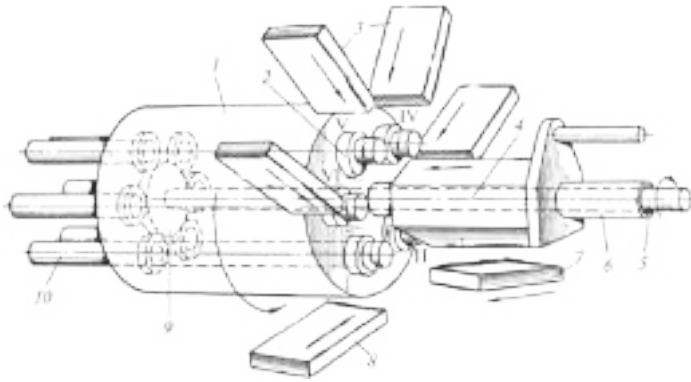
Схема роботи горизонтального багатошпindelьного токарного автомата: 1 — шпindelний блок; 2 — шпindel; 3, 7, 8 — поперечні супорти; 4 — повздовжній супорт; 5 — приводний вал; 6 — центральна гільза; 9 — центральне зубчасте колесо; 10 — напрямна труба
